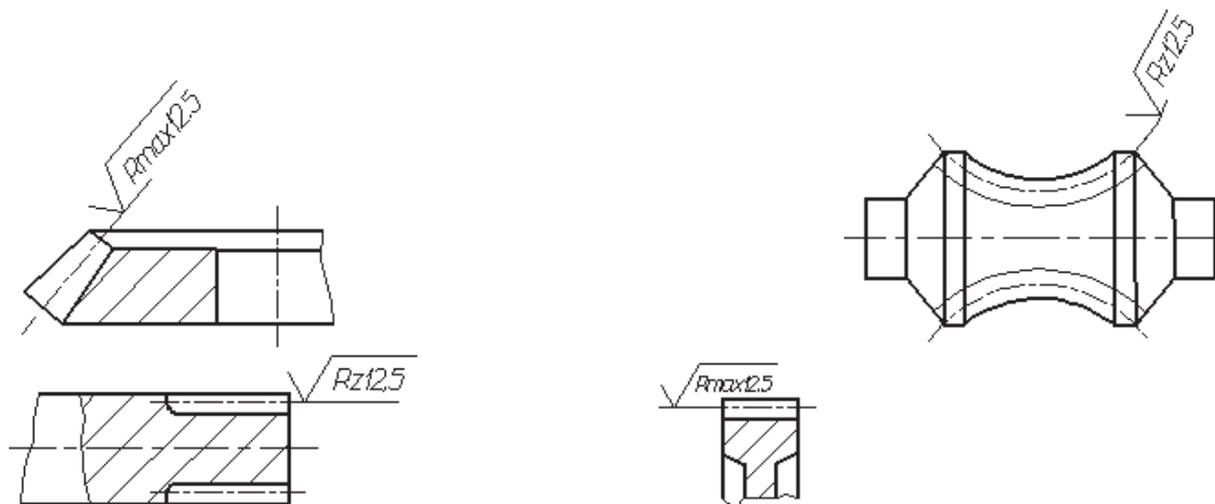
Примеры обозначения шероховатости рабочих поверхностей зубьев
